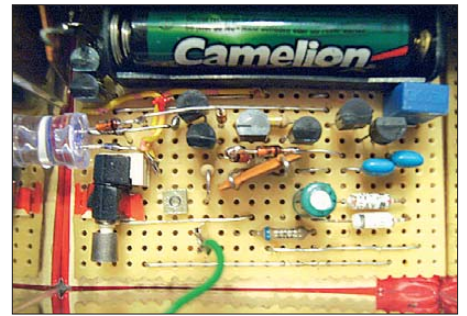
Das Nachweisgerät wurde auf einer Universalplatine aufgebaut.
